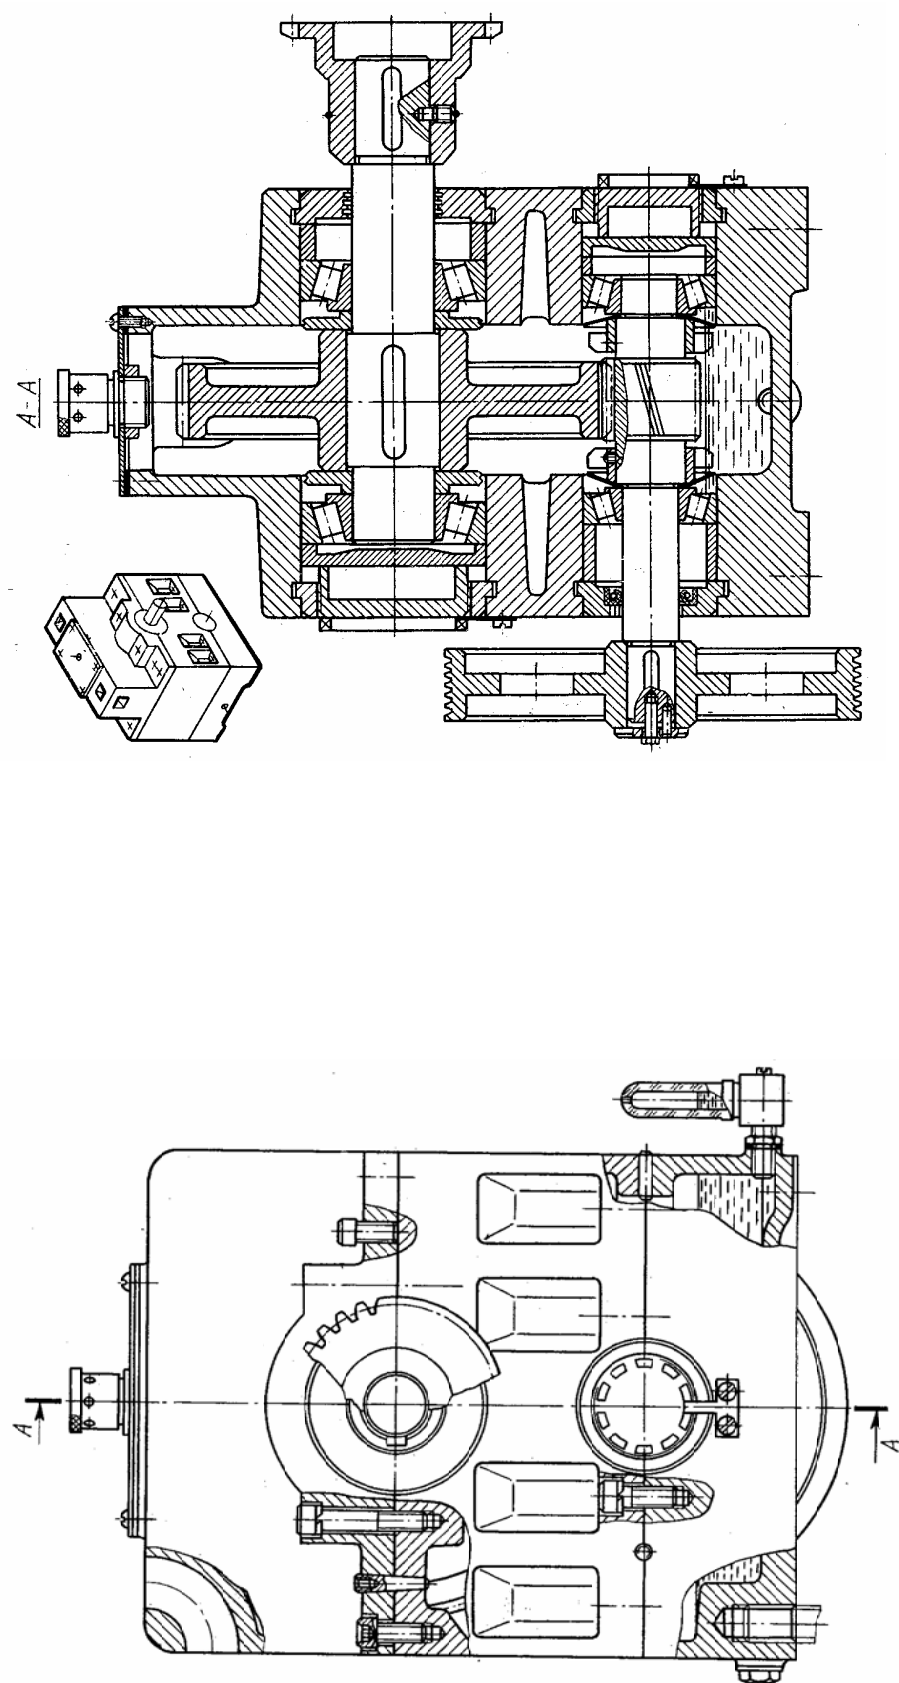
Редуктор (А7) цилиндрический одноступенчатый вертикальный с нижним расположением шестерни
